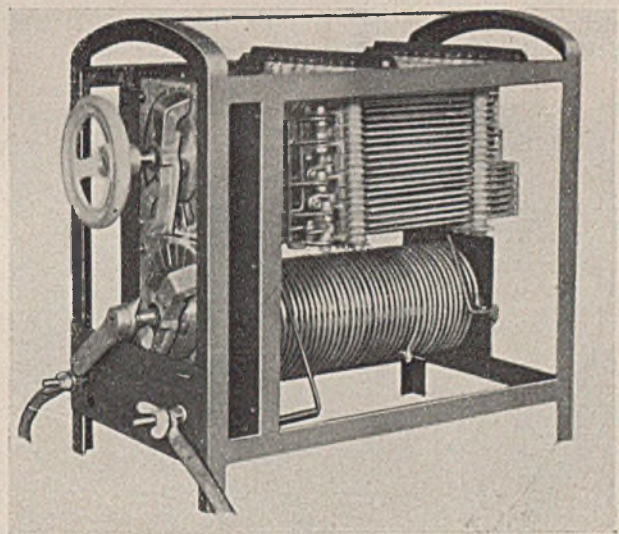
Schweißstromregler der Kjellberg Elektroden u. Maschinen G. m. b. H. Ummantelung abgenommen.
